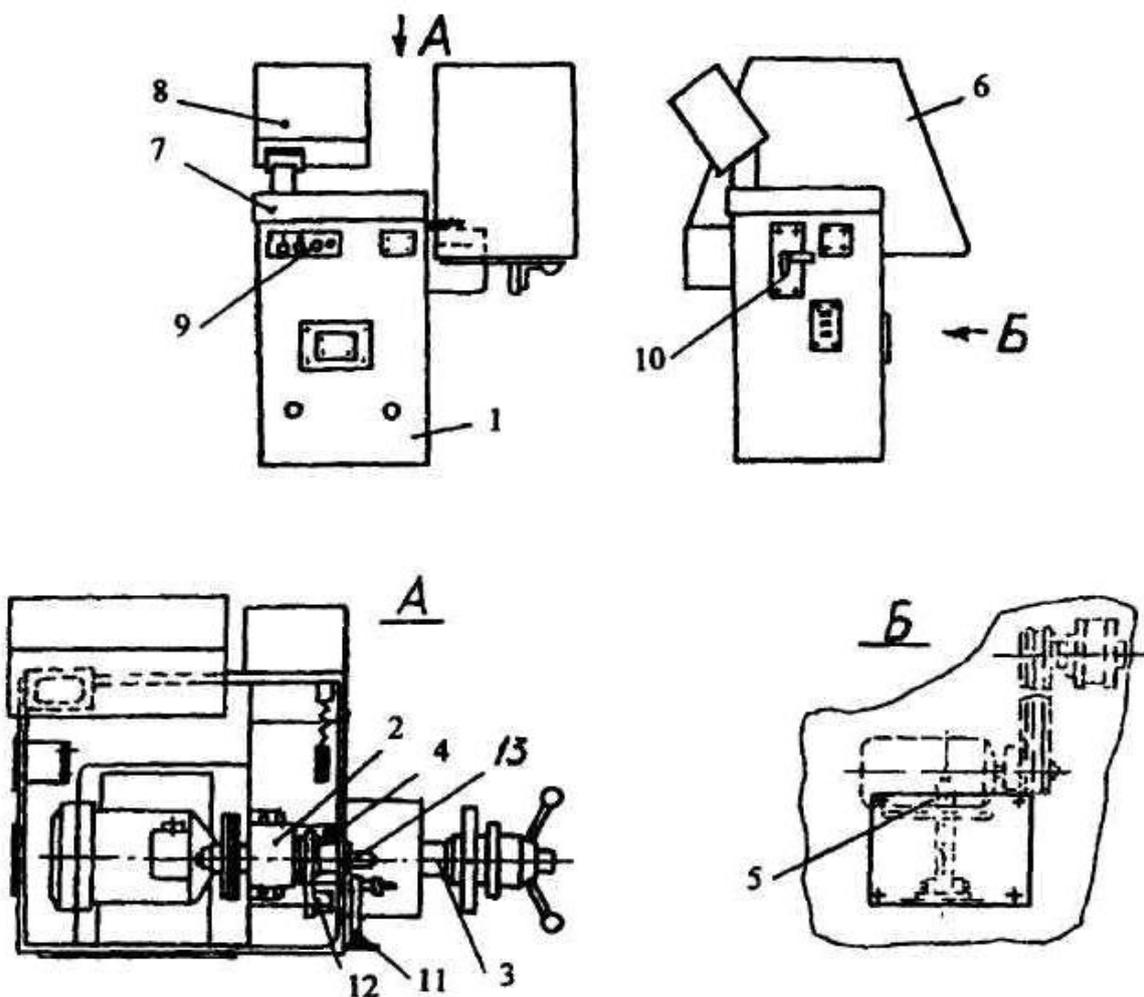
Общая компоновка балансировочного станка модели БМ
